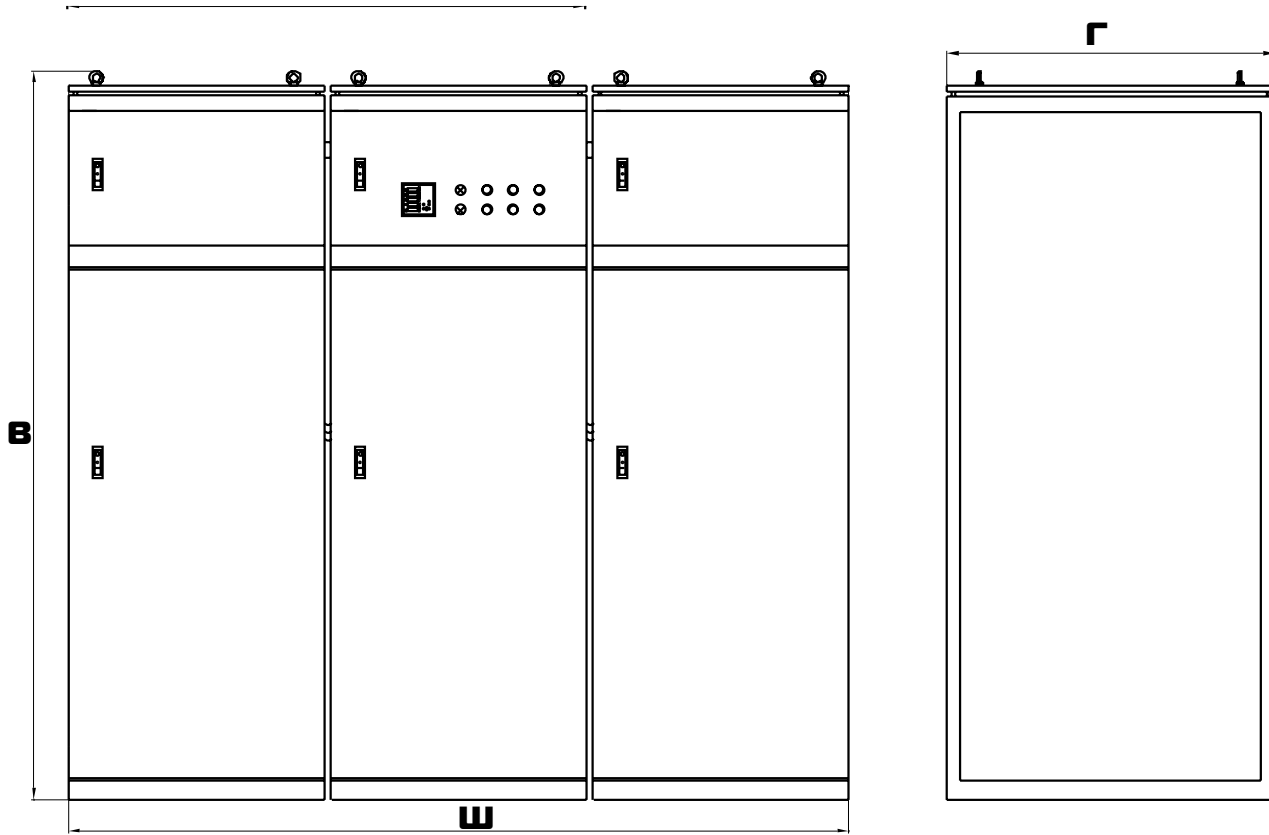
Габаритный чертеж трехфазного СТЭМ-2 IP20 800, 1000 кВА
